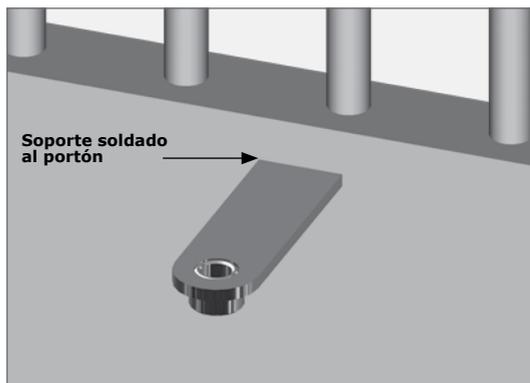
SOPORTE SOLDADO AL PORTÓN
